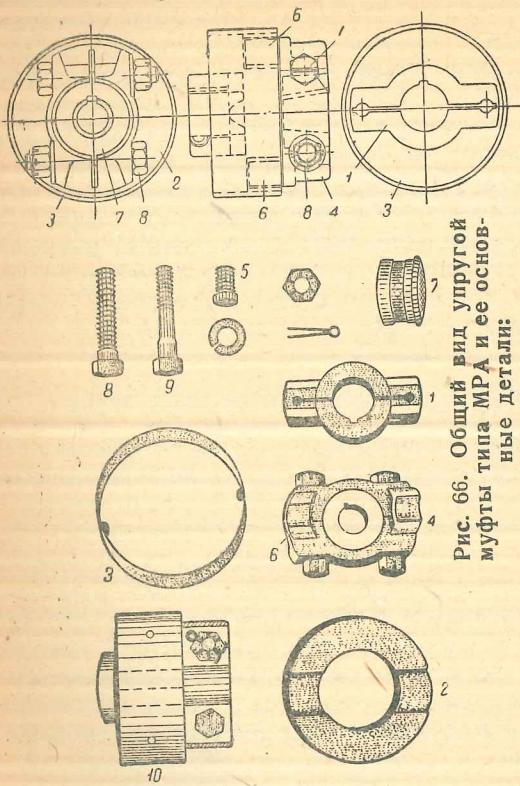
Общий вид упругой муфты типа МРА и ее основные детали:
